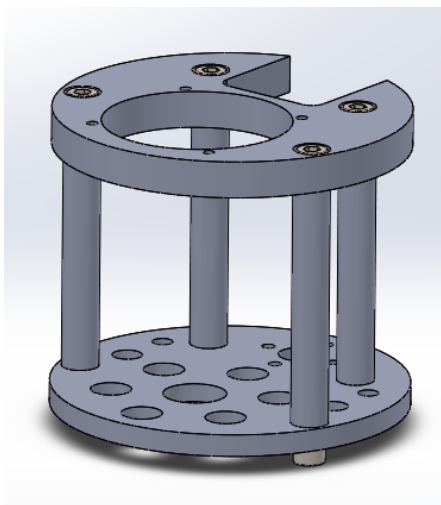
Estrutura da prensa sujeita a cargas elevadas.
